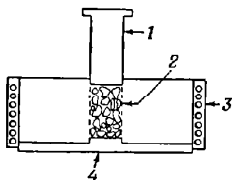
Пресс-форма для формования дисков и цилиндров.
